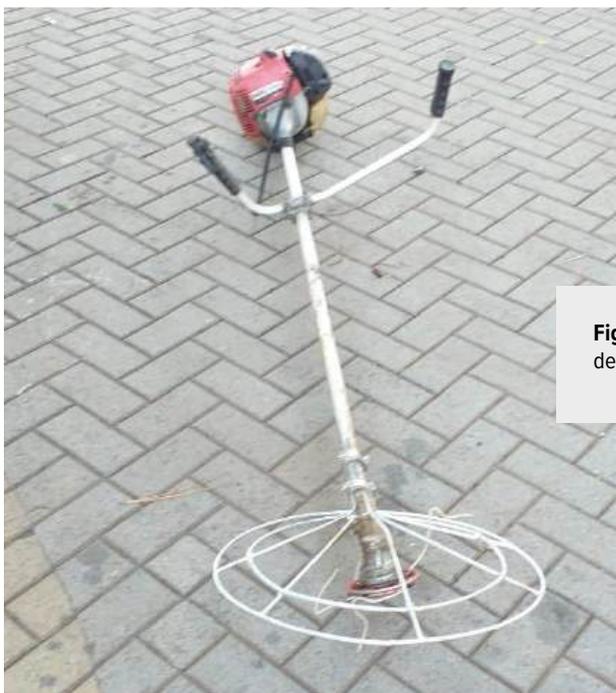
Instalación de anillo protector a chapeadora de cable. Fuente: Fabricio Ballestero
